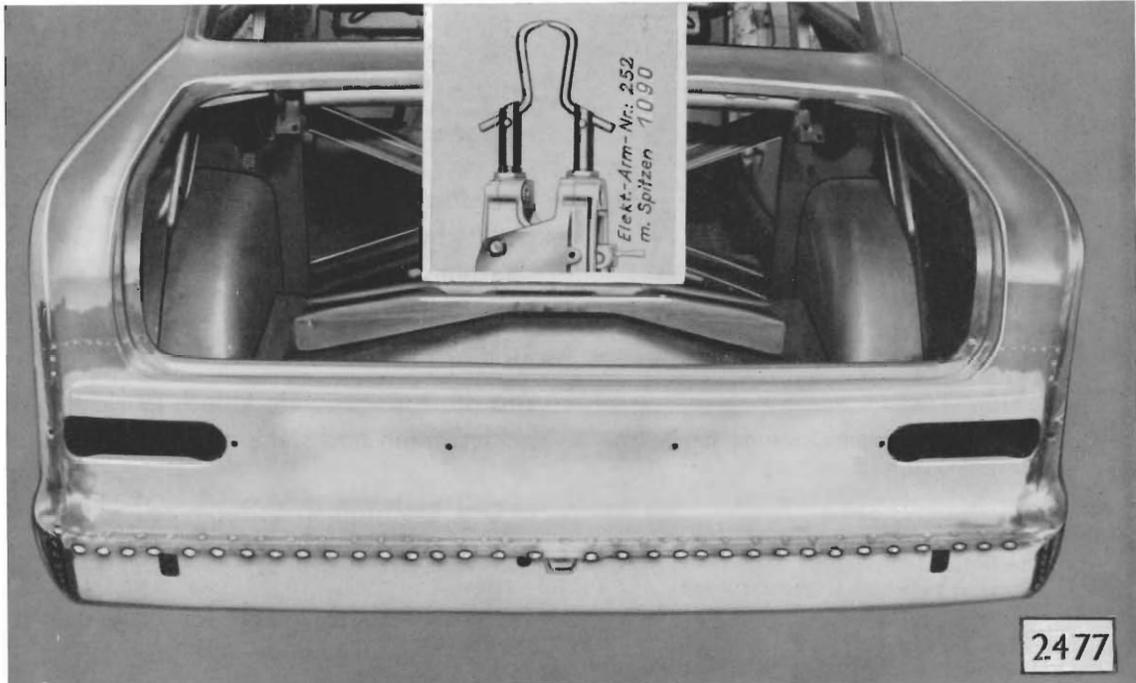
Stoßstangenabdeckblech am Bodenblech zangenpunktgeschweißt
